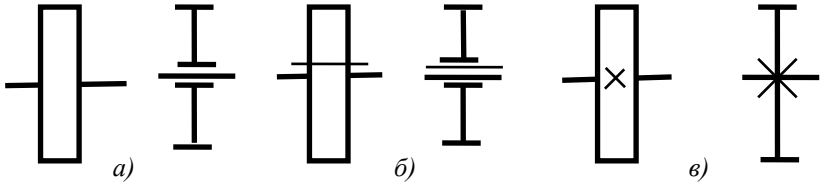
Соединения зубчатого колеса с валом
